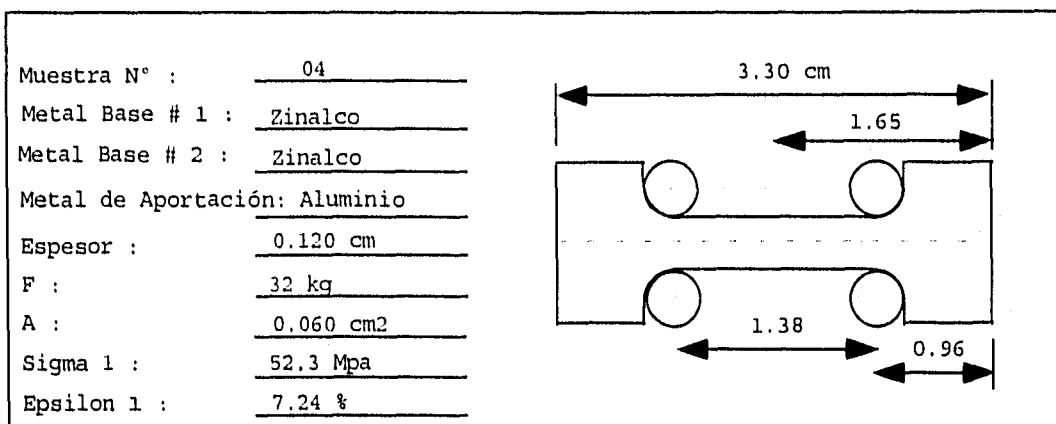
Probeta No.4, valores de prueba a la tensión para soldadura realizada entre Zinalco y Zinalco con material de Aporte Aluminio.
